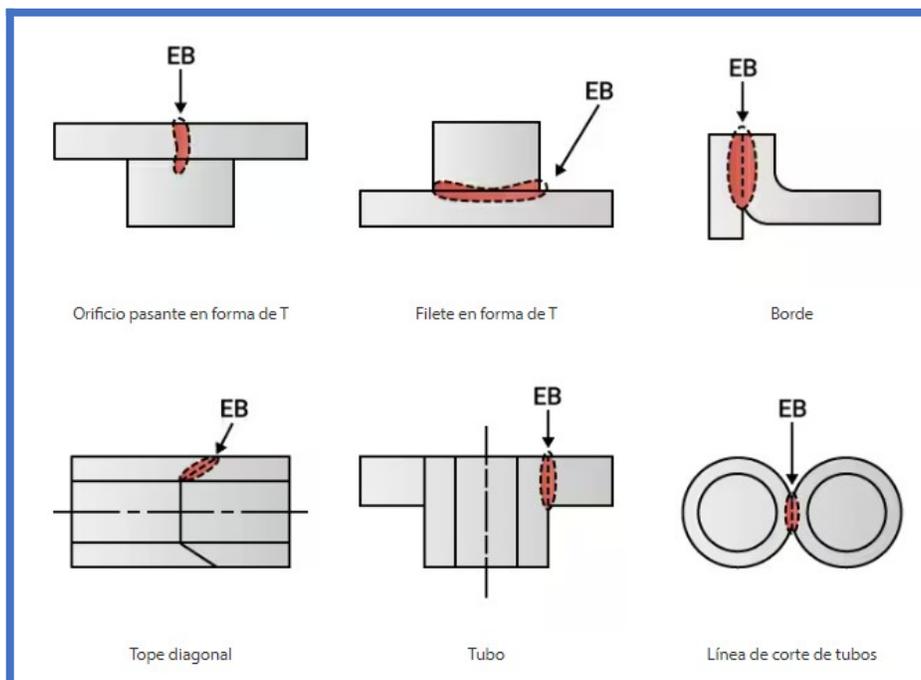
A y B Uniones de soldadura típicas posibles con la soldadura por haz de electrones (EB = HAZ DE ELECTRONES)
